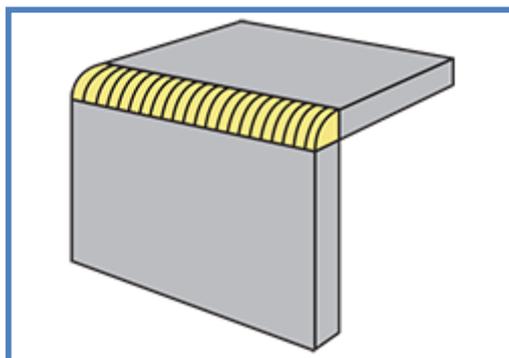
SOLDADURA JUNTA DE ESQUINA
